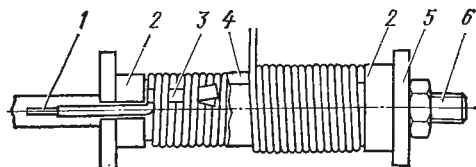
Намотка двухслойной цилиндрической обмотки НН трансформатора напряжения НОМ-35-66:
